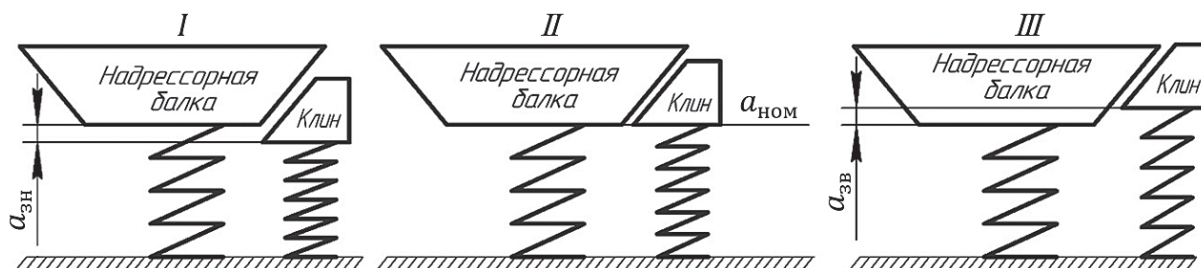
Конструктивно возможное положение опорной поверхности клина относительно опорной поверхности надрессорной балки:
